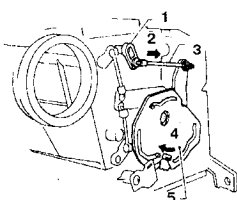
Регулировка соединительного механизма воздушной заслонки подачи горячего воздуха на ветровое стекло (См. Раздел 13)
